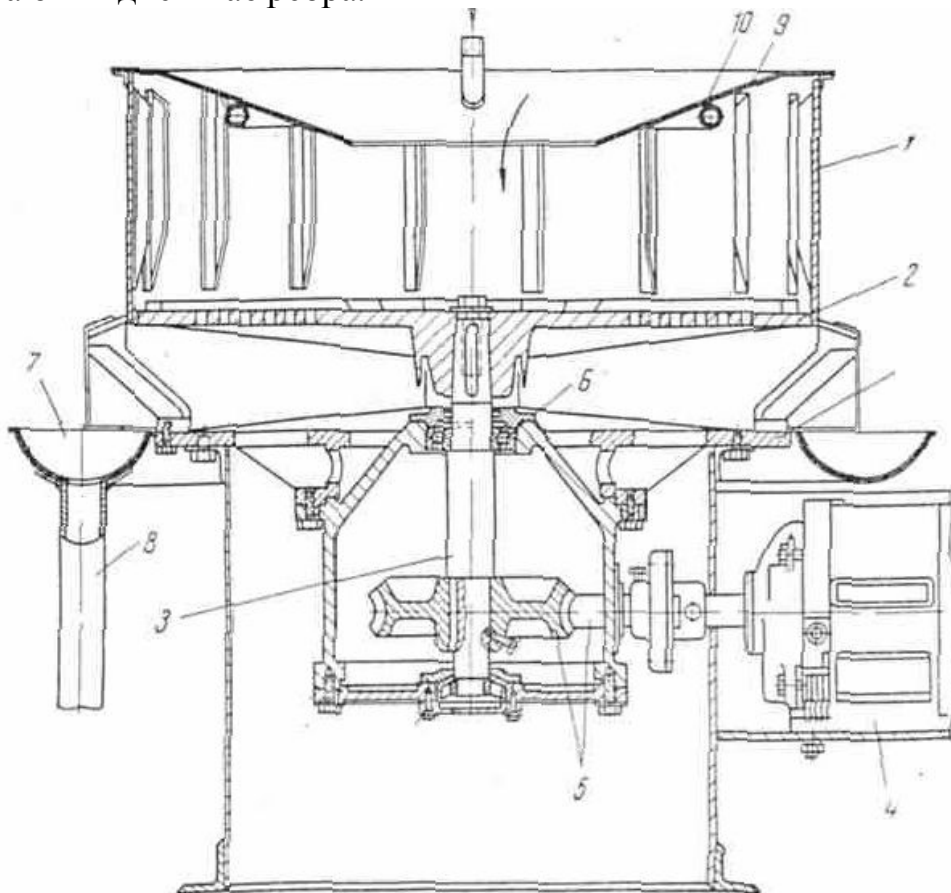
Центрифуга для обробки шерстних субпрордуктів
